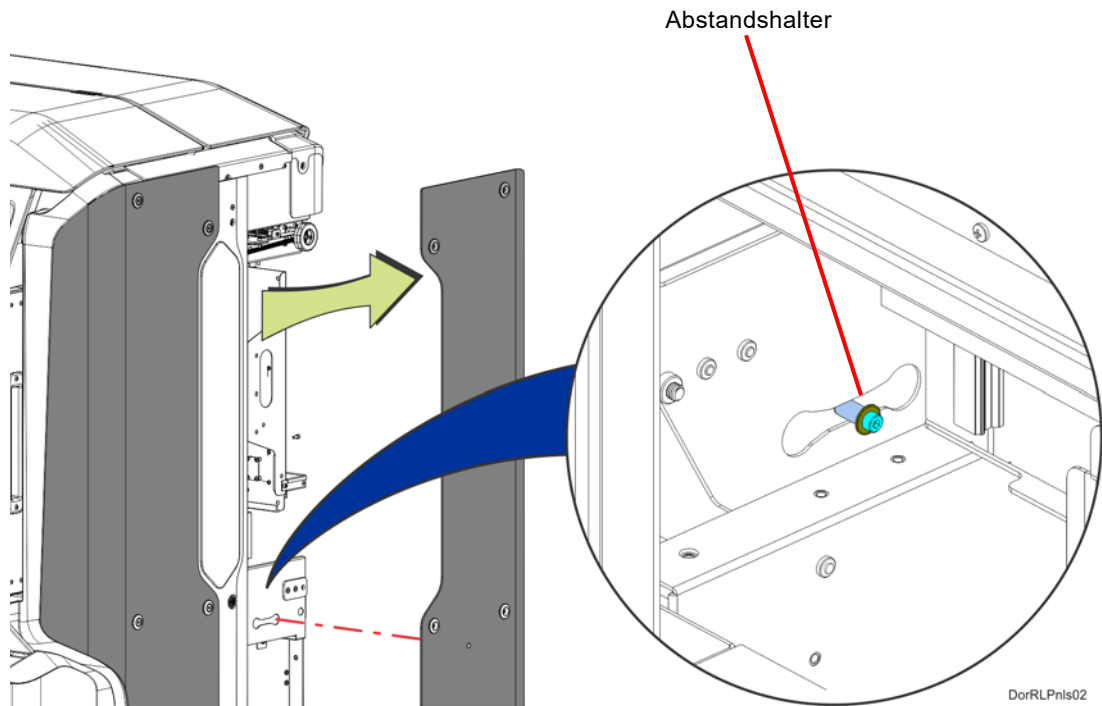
Positionen der Befestigungsschrauben für die Seitenpanels
